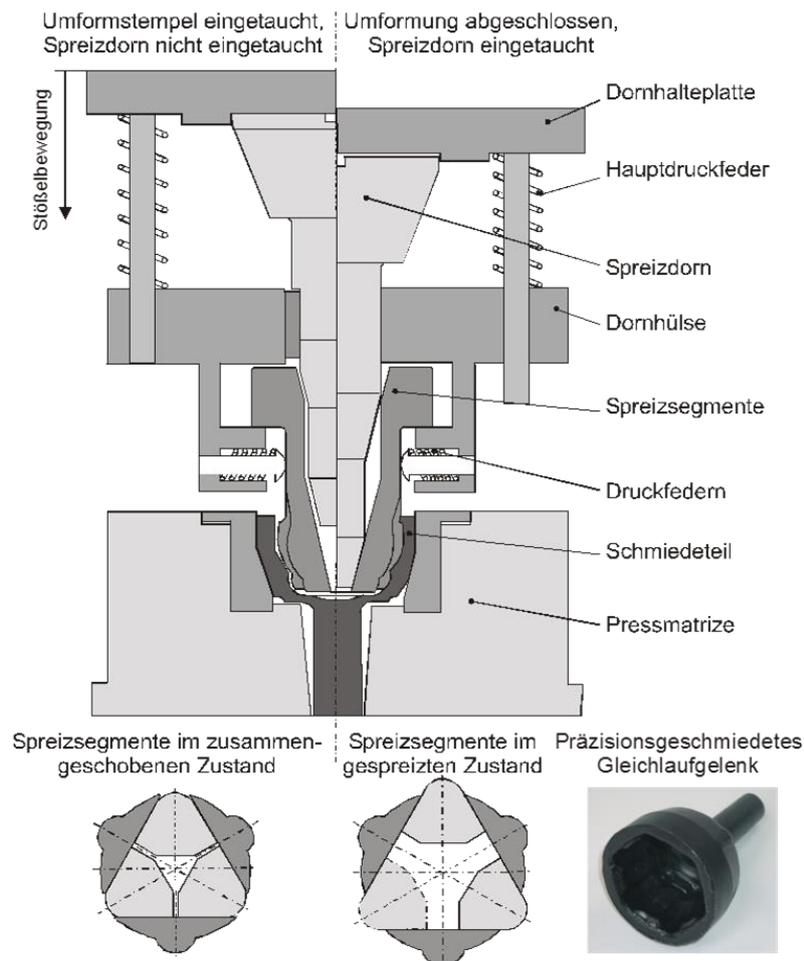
Werkzeugsystem der dritten Formgebungsstufe zum Präzisionsschmieden hinterschnittener Gleichlaufgelenke [Wie96]
